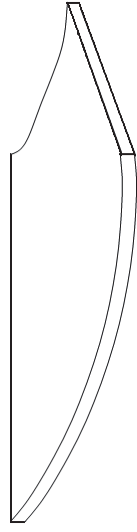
Вид готовой подложки для формирования наружной обшивки
